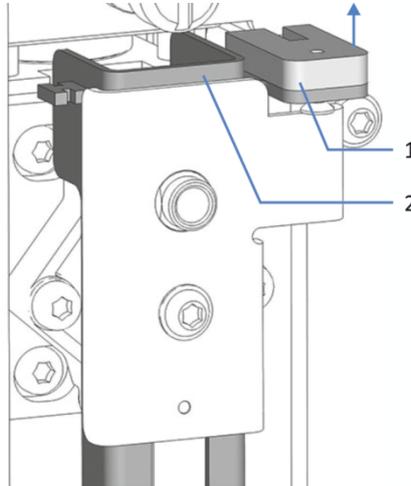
Déplacement du verrou du pousseur de flacon vers le haut
